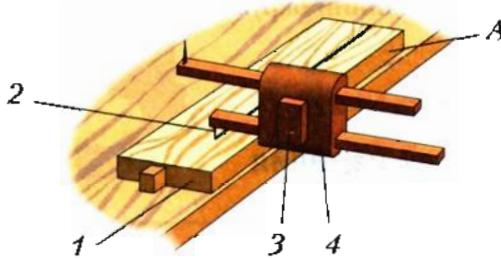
Разметка брусков рейсмусом: 1 – заготовка; 2 – ножка рейсмуса; 3 – клин; 4 – корпус рейсмуса; *A* – базовая кромка
